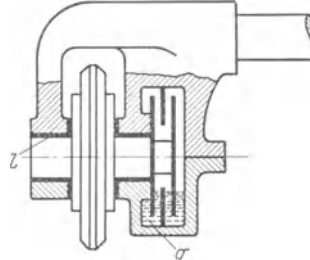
Schlepprolle ohne stromführende Gleitlager. l = isolierte Lauflager; q = Stromzuführung durch Quecksilber.
